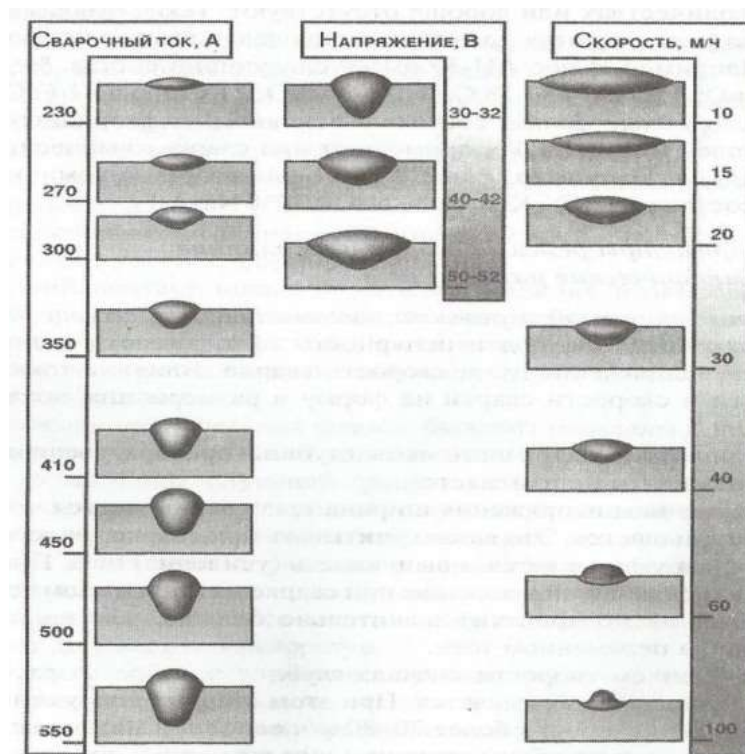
Влияние сварочного тока, напряжения и скорости сварки на форму и размеры сварного шва
